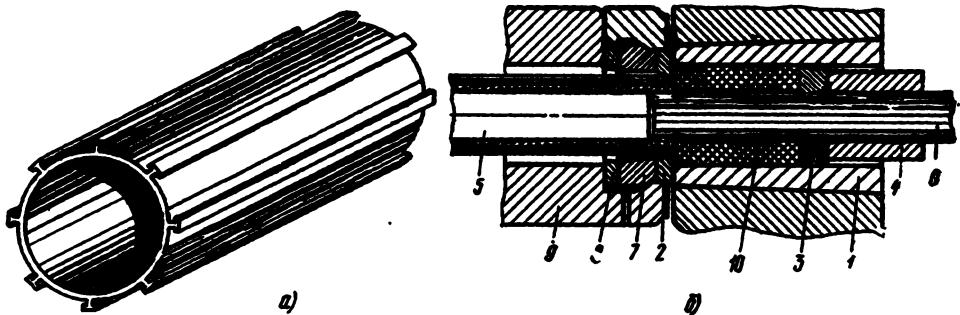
Схема прессования б цилиндрической ребристой панели а:
